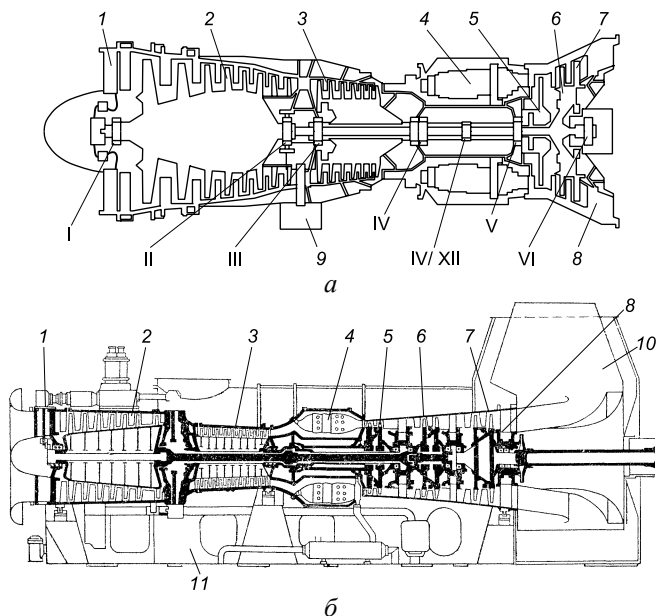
Схемы расположения подшипников роторов и силовых элементов (корпусов) опор трехвалных авиапроизводных ГТУ FT8 (а) и SGT-500 (б) (I–VI – различные виды подшипников):
